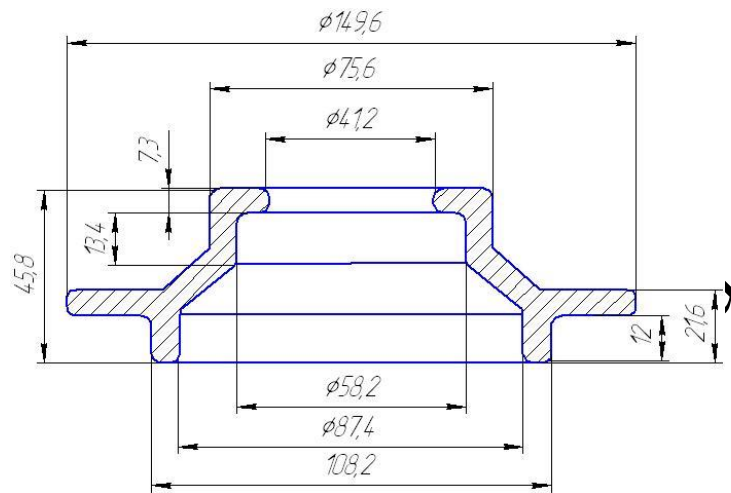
Ескіз заготовки при литті в оболонковій формі
